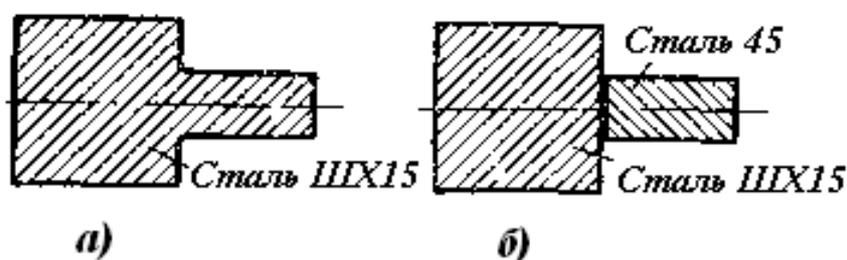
Изготовление калибров по старой технологии (а) и с применением сварки трением (б)
